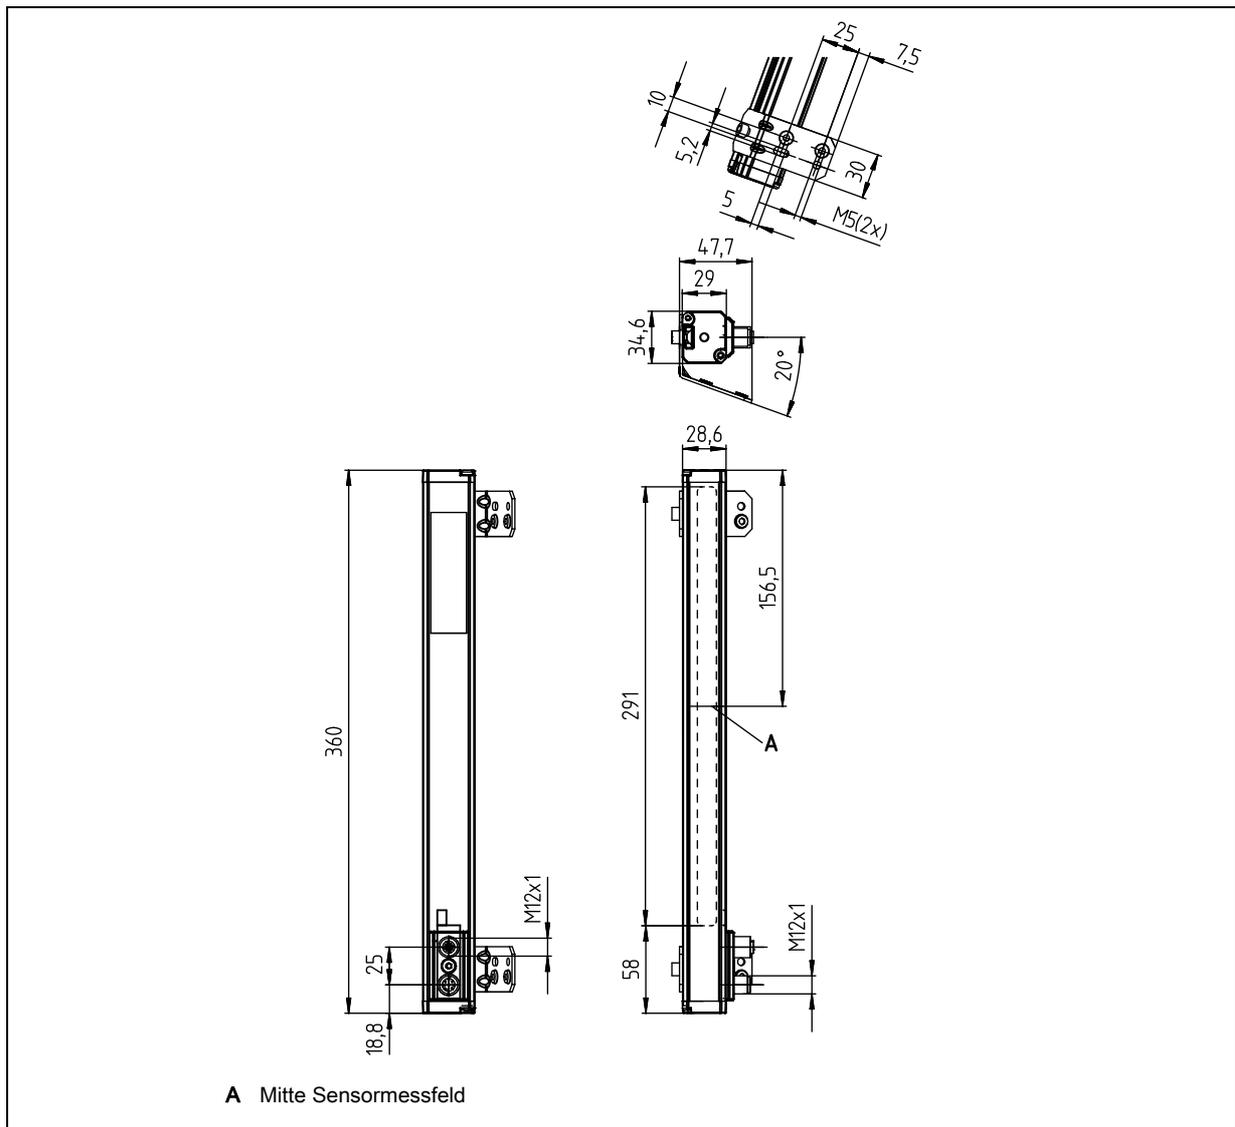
Maßzeichnung OGS 600-280/CN-M12 – lange Ausführung
